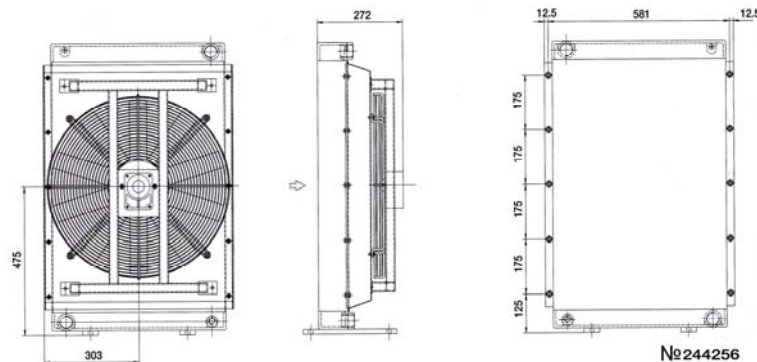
Габаритные и присоединительные размеры теплообменника HPA 42.
